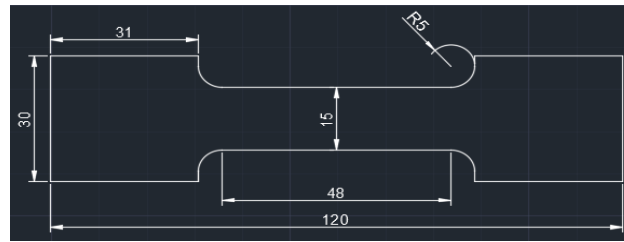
Desenho em AutoCAD (Fonte: Autores)
